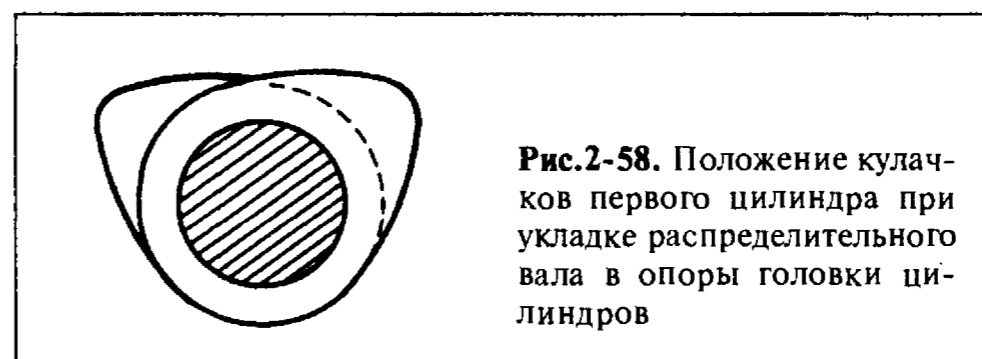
Положение кулачков первого цилиндра при укладке распределительного вала в опоры головки цилиндров
